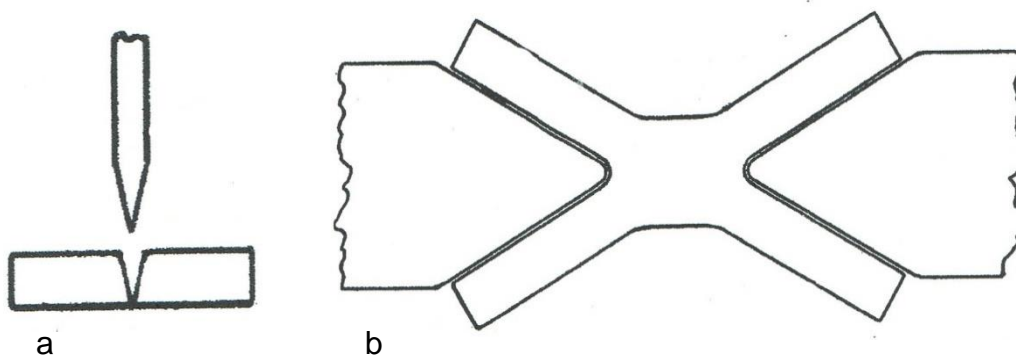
Spreizwerkzeuge: a) Werkzeug zum Schlitzern des Ausgangsprofils, b) Zwei Keile zum Spreizen der Magnetschenkel
